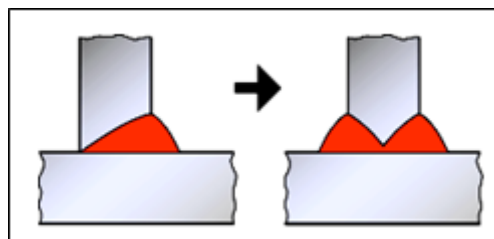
Configuration du Joint, les soudures à deux faces sont moins susceptibles.
